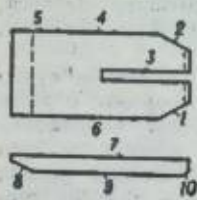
Понтон: 1 — носовой свес; 2 — прорез; 3 — левый борт; 4 — корма; 5 — правый борт; 6 — палуба; 7 — носовая свеса; 8 — днище; 9 — кормовая свеса; 10 — носовая свеса.
